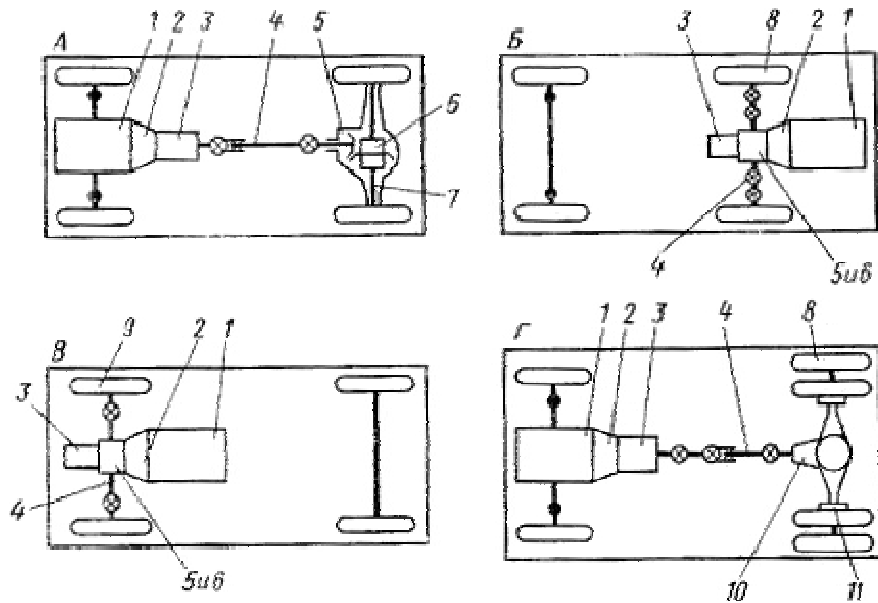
Ступенчатые механические трансмиссии автомобилей типа 2х1 с различным расположением двигателя: А и Г - легковые и грузового заднеприводных с расположением двигателя; Б - легкового заднеприводного с задним расположением двигателя; В - легкового переднеприводного с передним расположением двигателя
